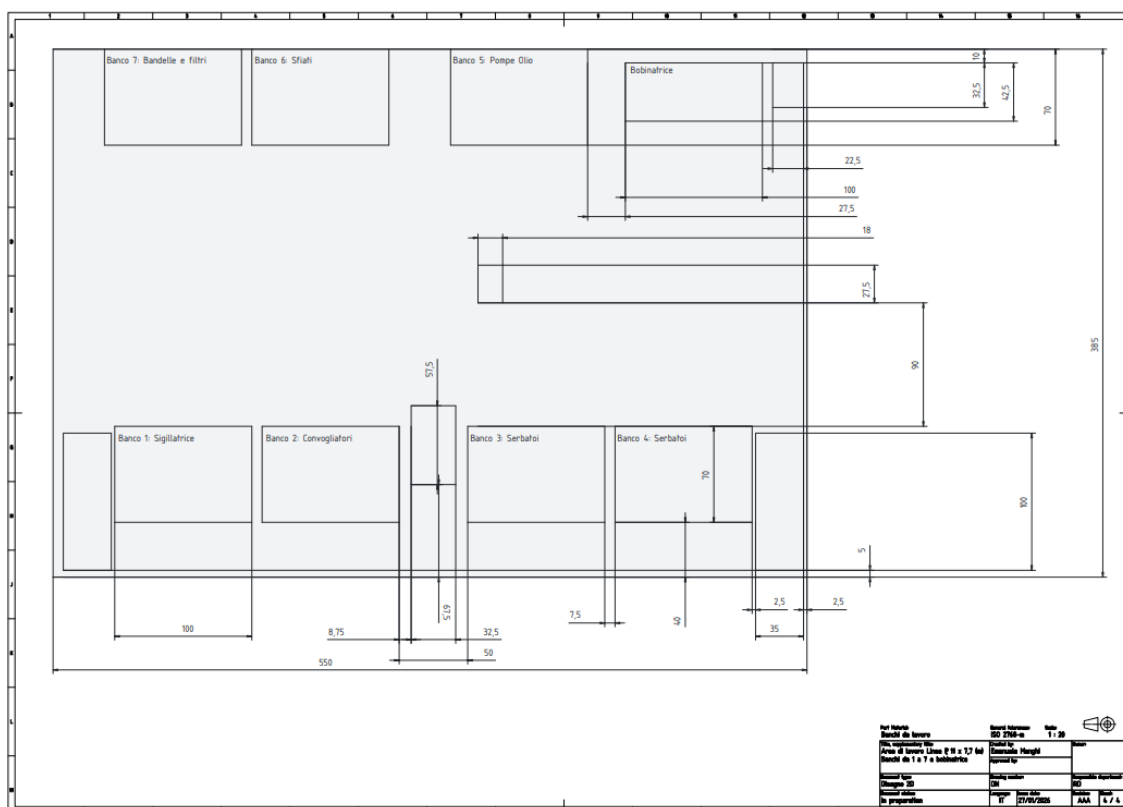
Layout della postazione accorpata di premontaggio con disposizione dei banchi e area centrale per la movimentazione dei pallet
